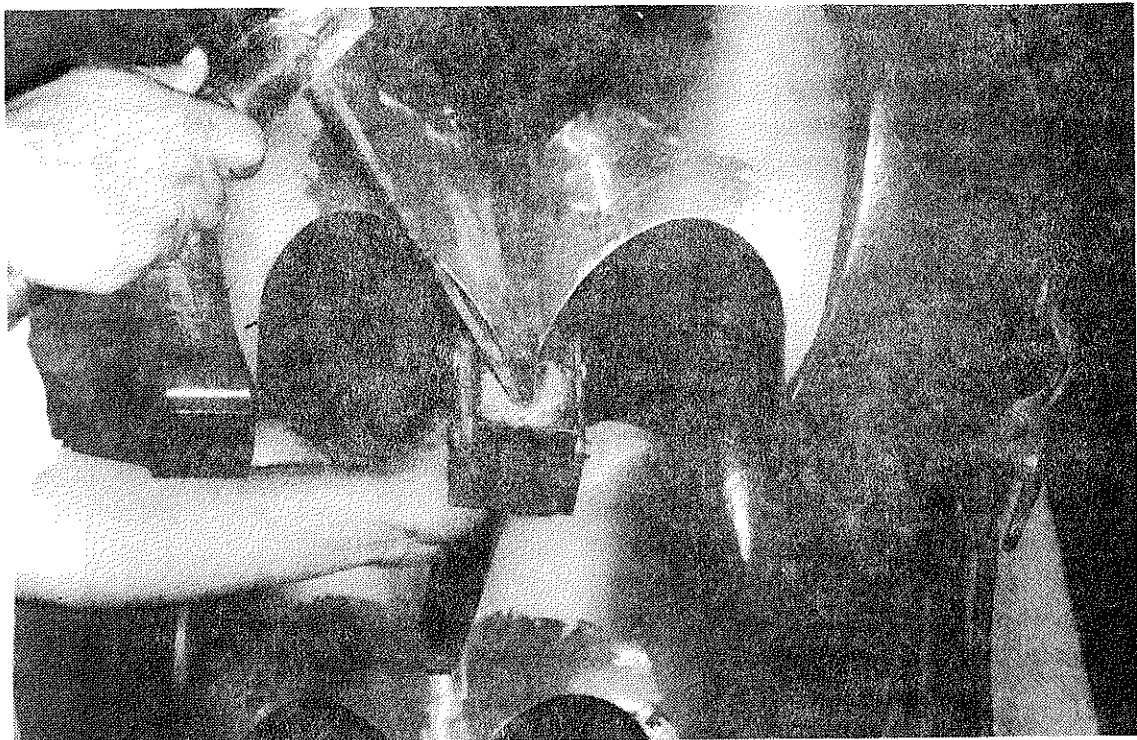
Inicio de la soldadura apoyada con una plantilla de cobre
